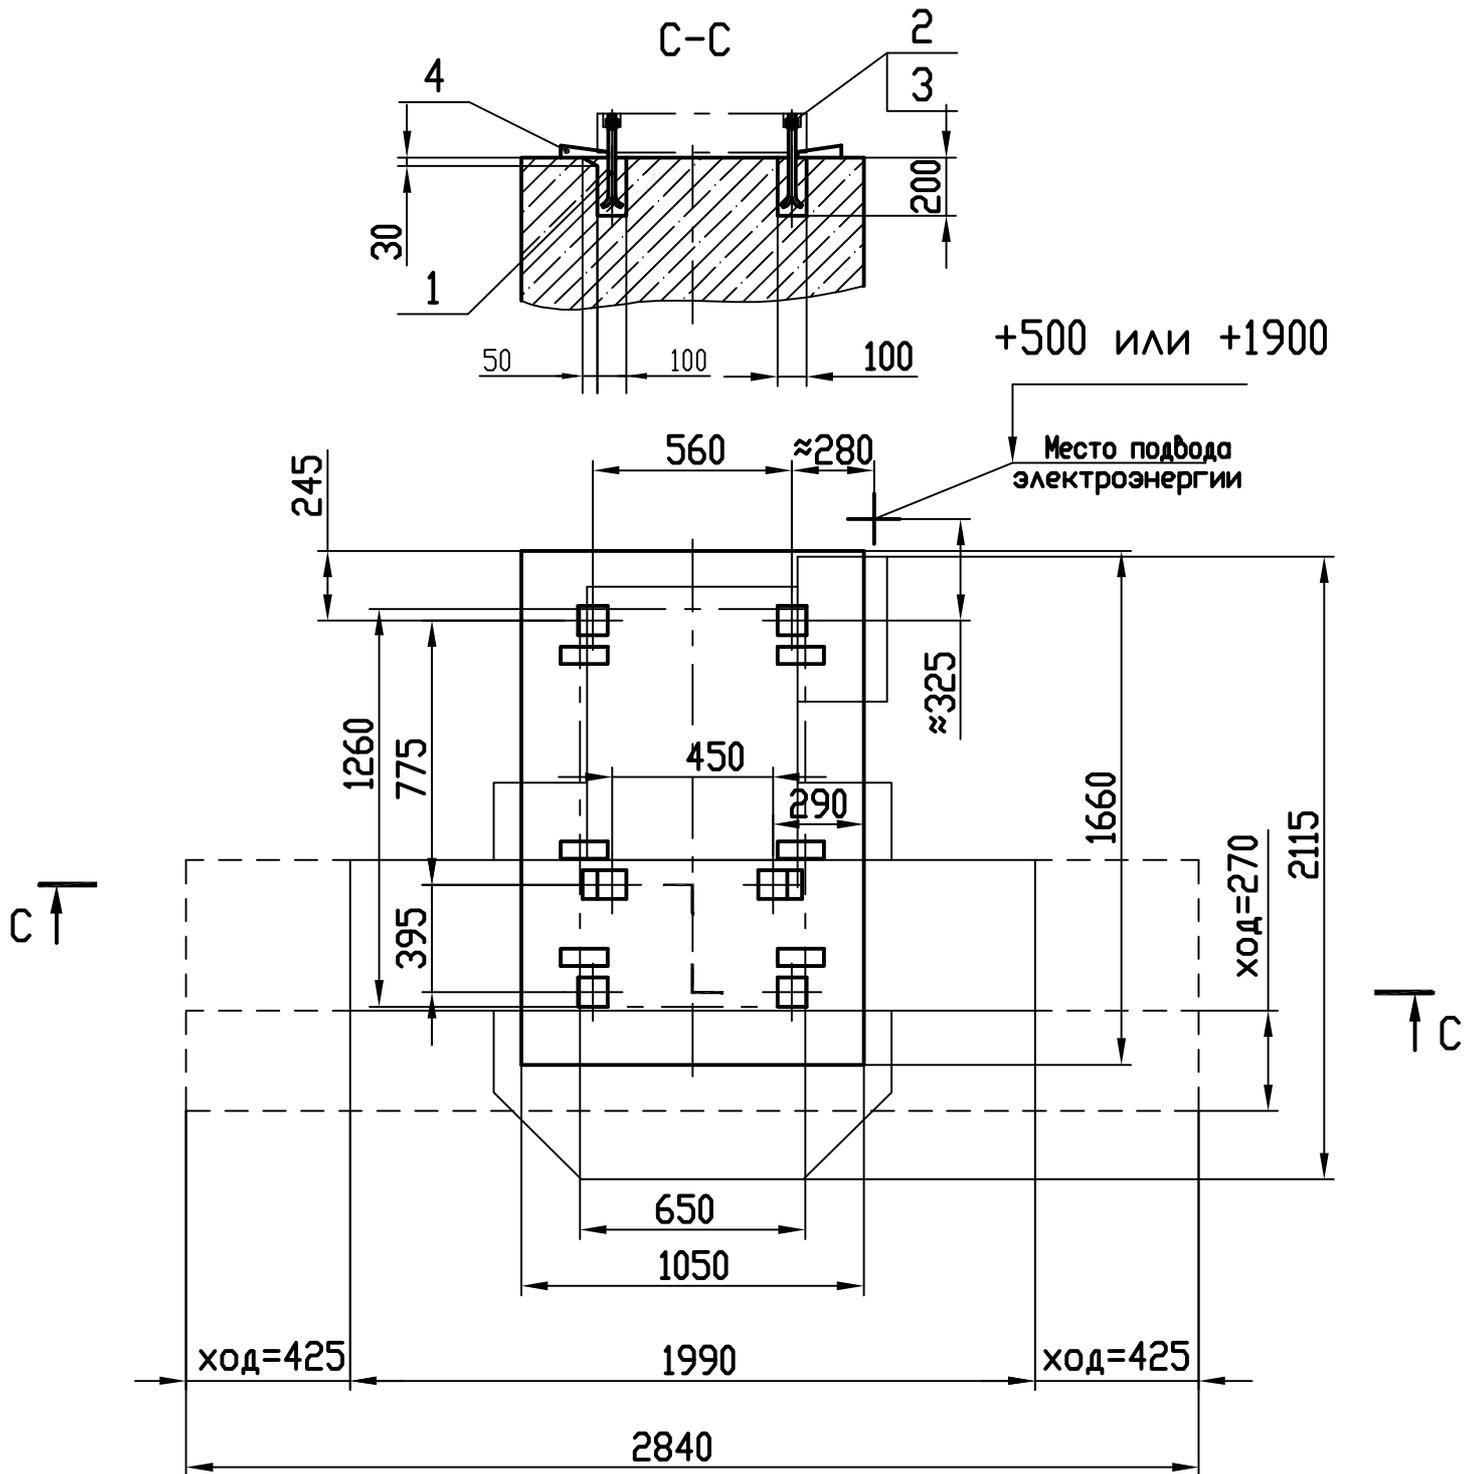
Монтажный чертеж для станков мод. FSS350MR, FSS350MRNC
